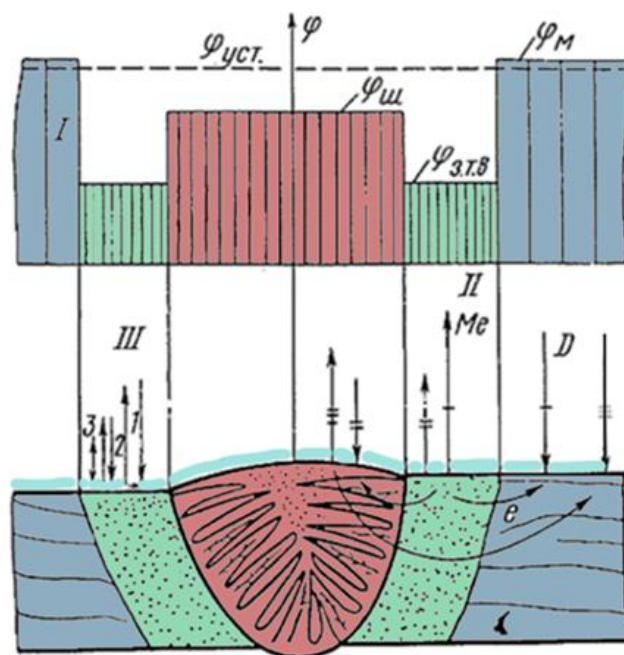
Схема электрохимической коррозии сварного соединения:
